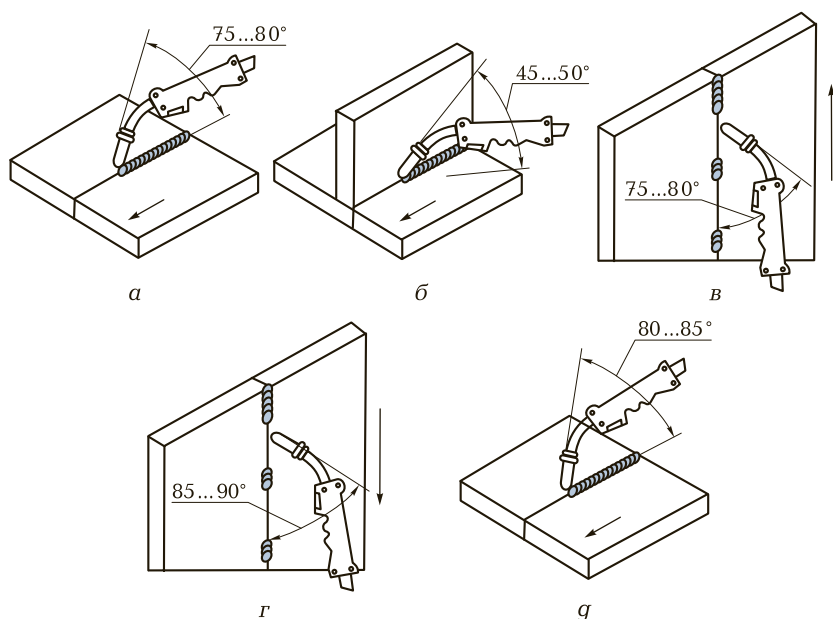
Угол наклона сварочной горелки при выполнении различных швов в нижнем и вертикальном положениях при циклическом режиме сварки короткой дугой (а–г) и при струйном переносе металла (д)
